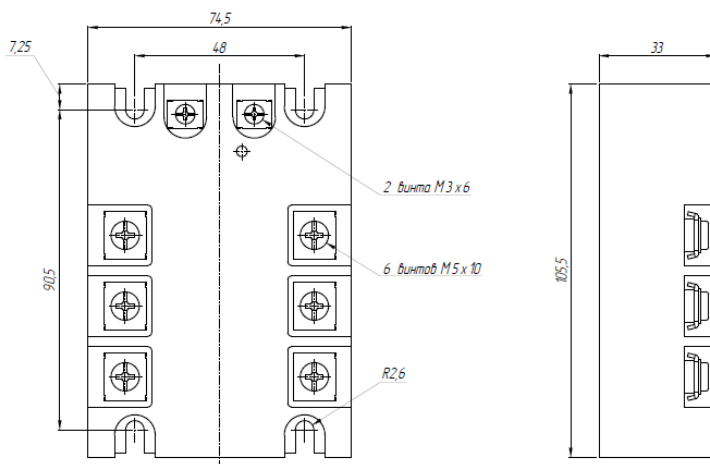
габаритные и установочные размеры ТТП серии HT-●●44.ZD3 / ZA2
